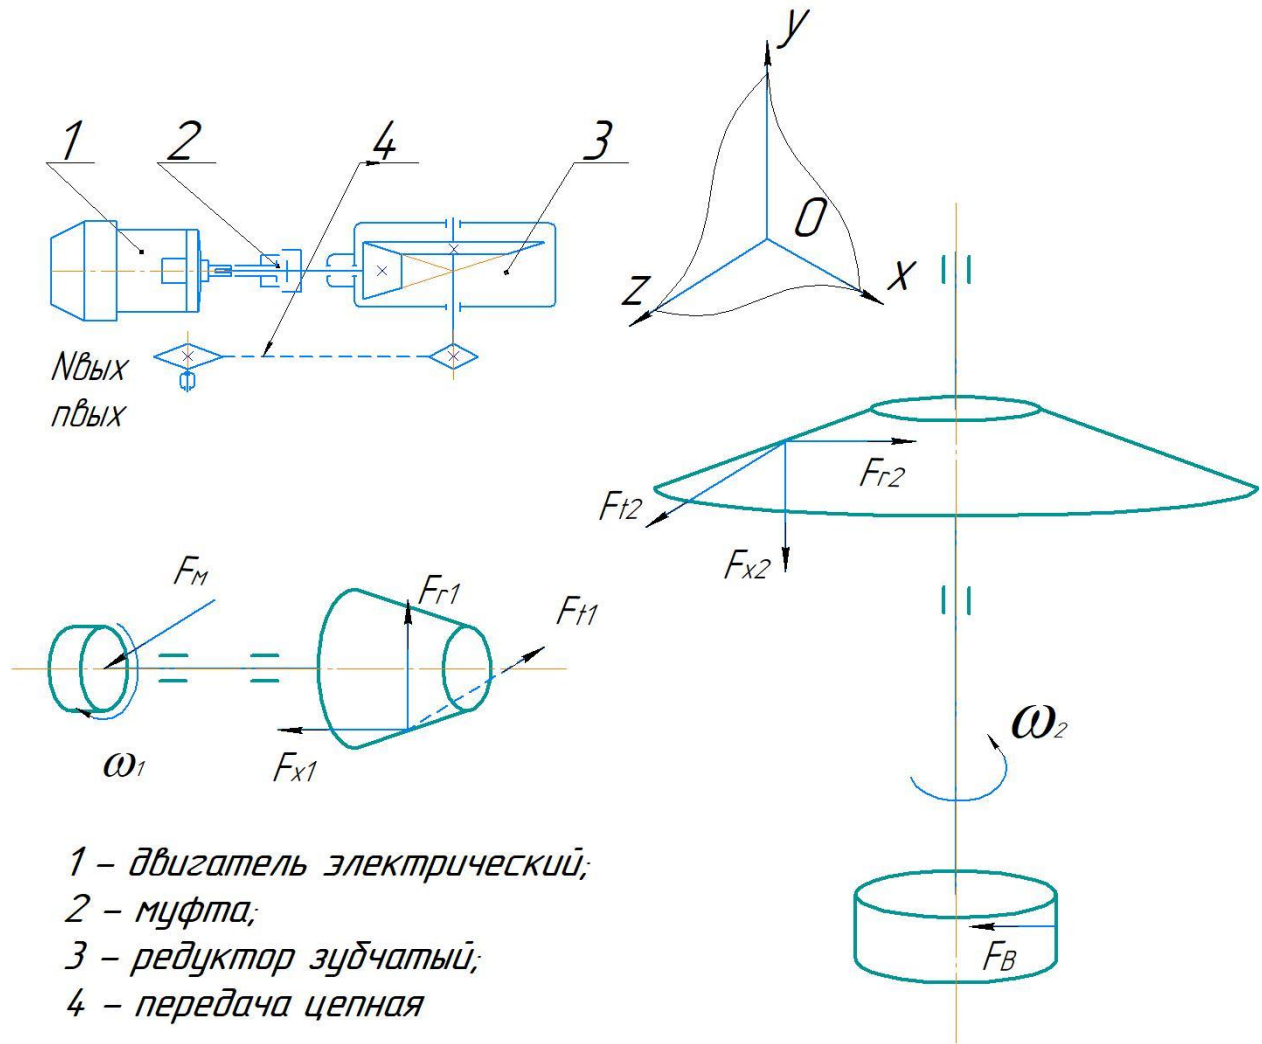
Направление сил в зацеплении закрытой конической и цепной передач
